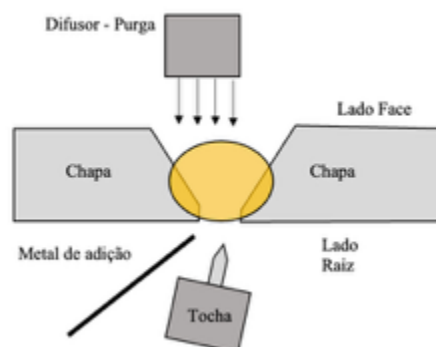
Croqui da soldagem do passe de raiz das chapas CP2A e CP2B com o processo GTAW.
